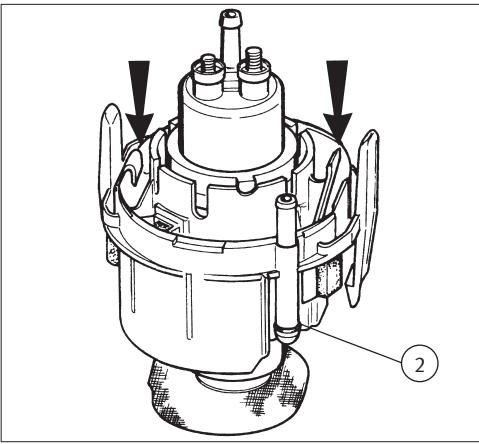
PIERBURG-Kraftstoffpumpe (Serie)
